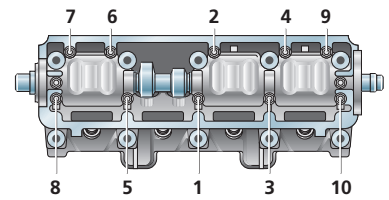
Порядок затягивания гаек крепления корпусов подшипников распределительного вала
